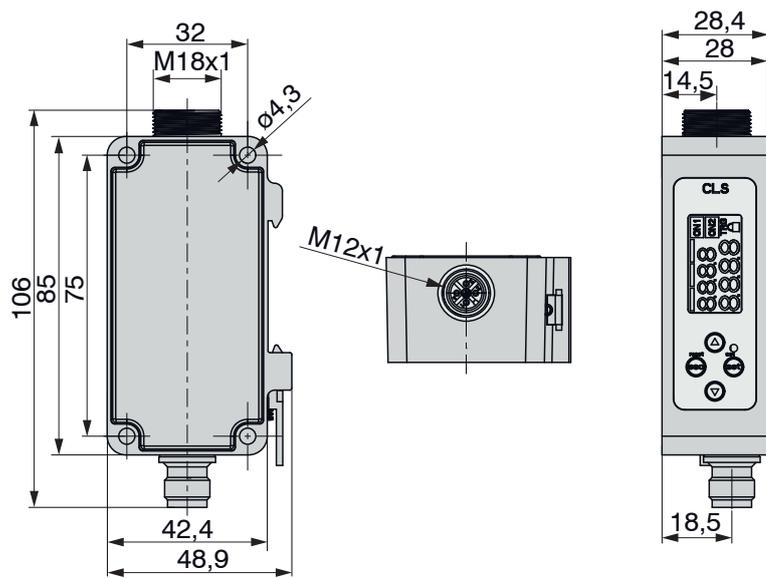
Maßzeichnung optoCONTROL CLS1000, Abmessungen in mm
